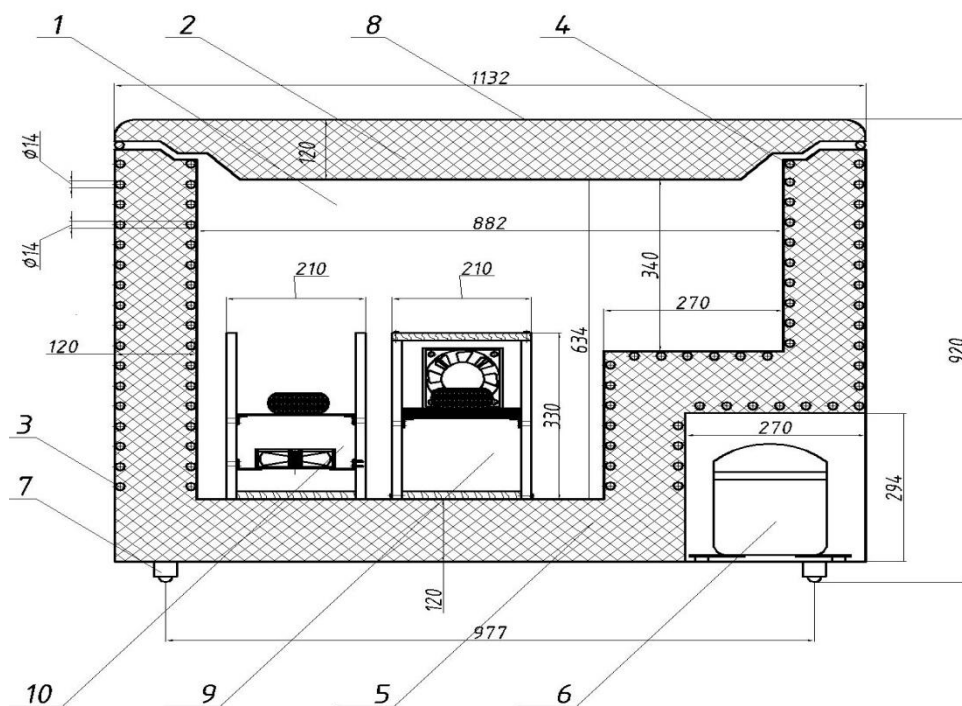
Лабораторный стенд: 1 – внутренняя камера; 2 – крышка холодильного ларя; 3 – конденсатор; 4 – испаритель; 5 – изоляционный слой; 6 – компрессор; 7 – колесная опора; 8 – корпус; 9 – туннель с металлическими плитами; 10 – туннель с металлической решеткой
